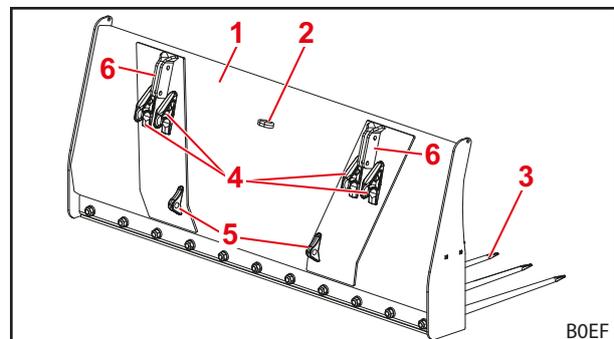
Estructura de la horquilla para estiércol (para cargador frontal FZ 60/60.1/80.1/100) – Vista posterior
